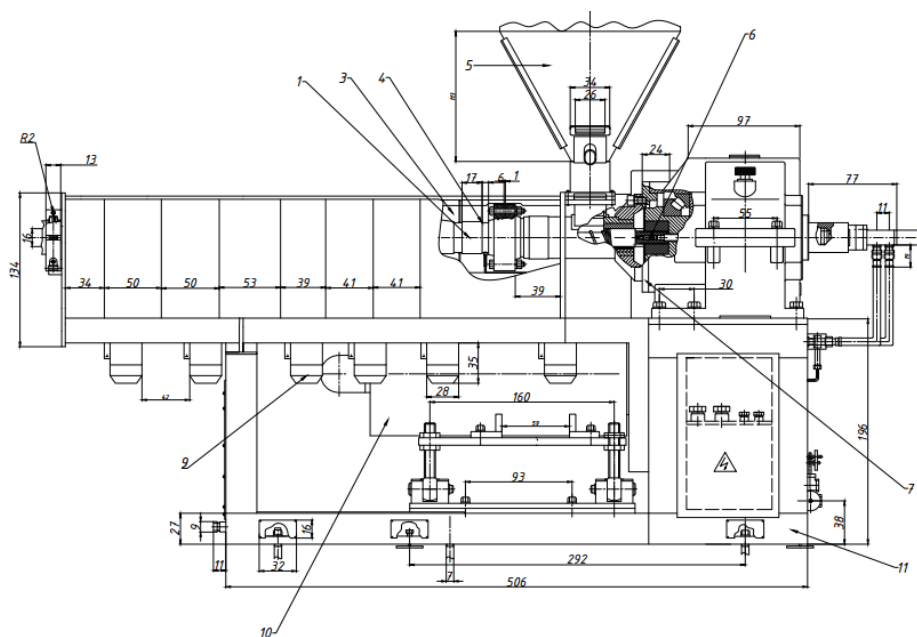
Загальний вигляд черв'ячного пресу: 1 – черв'як; 2 –редуктор;
